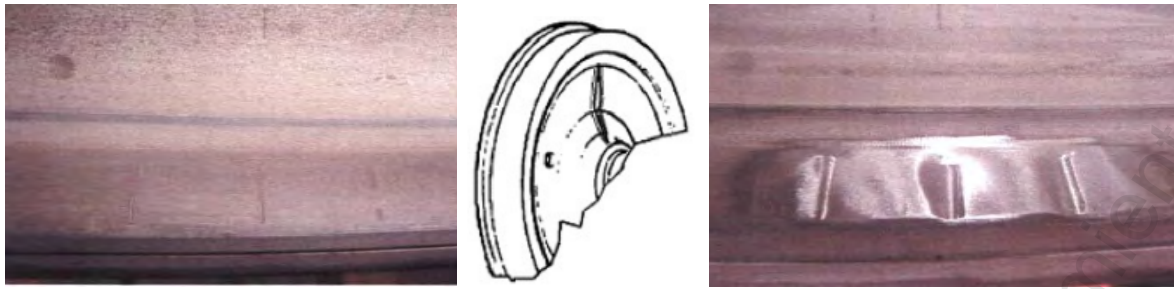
Fisuras en velo por entallas del mecanizado
